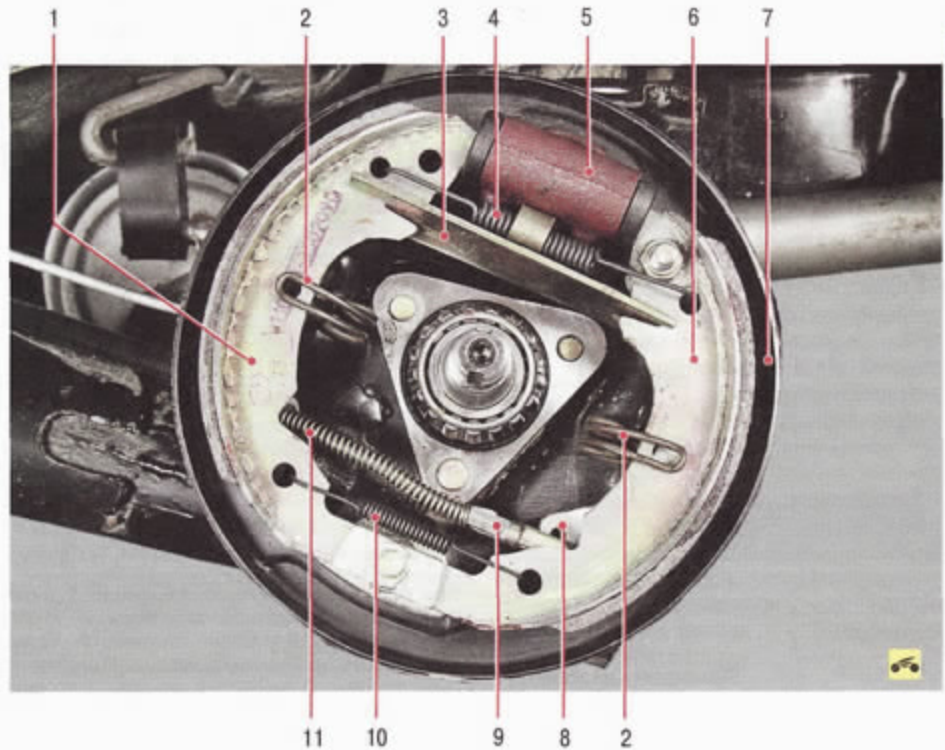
Детали тормозного механизма заднего колеса: 1 — передняя тормозная колодка; 2 — пружинная планка; 3 — распорная планка; 4 — верхняя стяжная пружина; 5 — рабочий тормозной цилиндр; 6 — задняя тормозная колодка; 7 — щит тормоза; 8 — разжимной рычаг привода стояночного тормоза; 9 — наконечник заднего троса привода стояночного тормоза; 10 — нижняя стяжная пружина; 11 — трос привода стояночного тормоза
